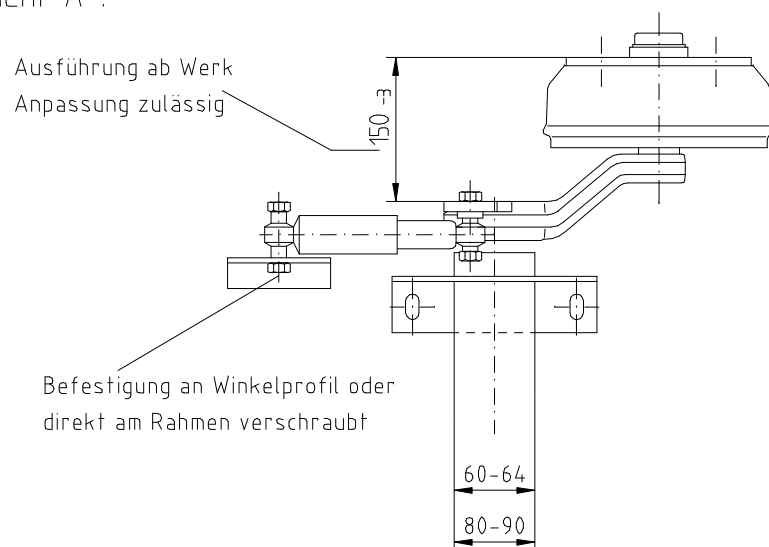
Aufbau der wasserdichten Ausführung im Detail
